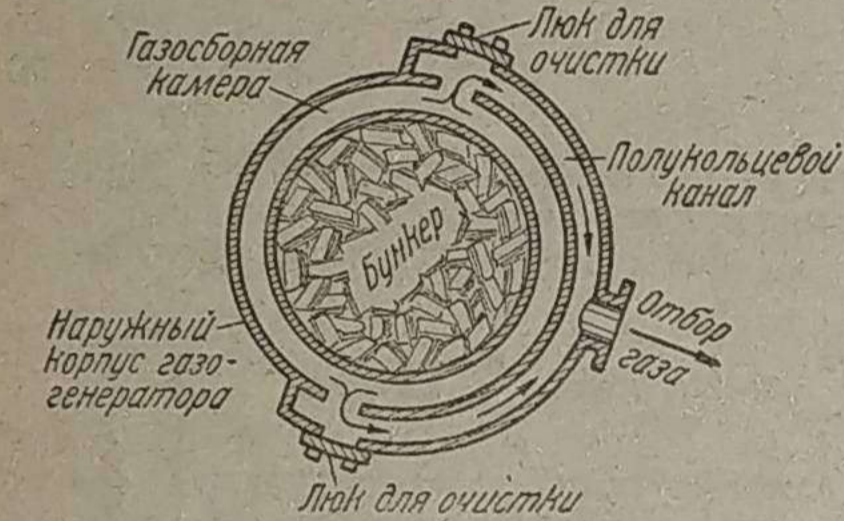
Газосборная камера и полукольцевой канал (вид сверху в разрезе)
